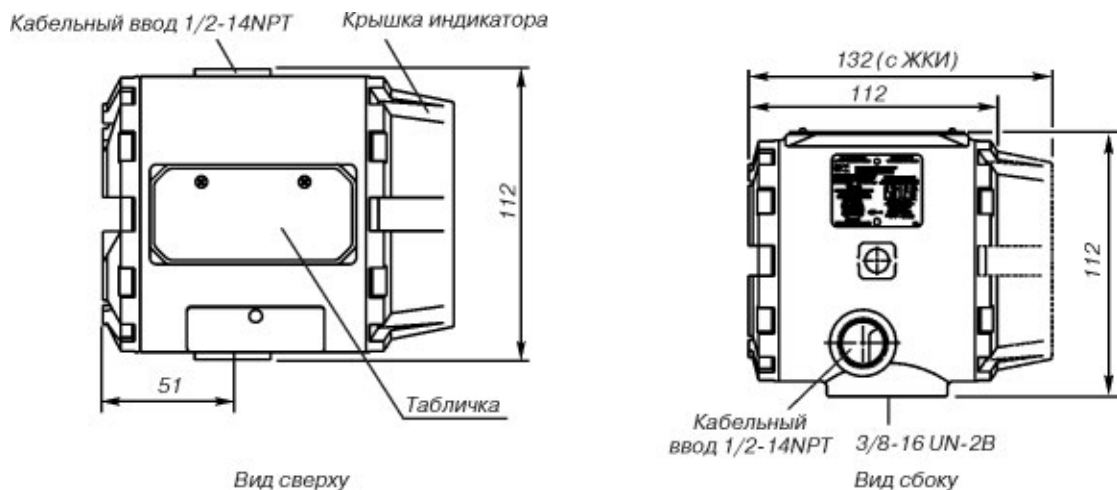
Габаритный чертеж преобразователя. Кабельный ввод 1/4-NPT*.
